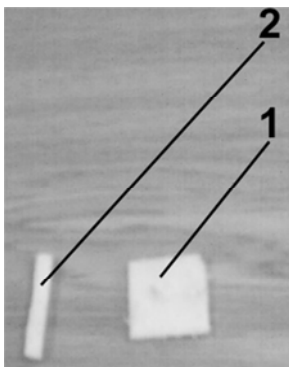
Фотография образцов, используемых для сварки трением
